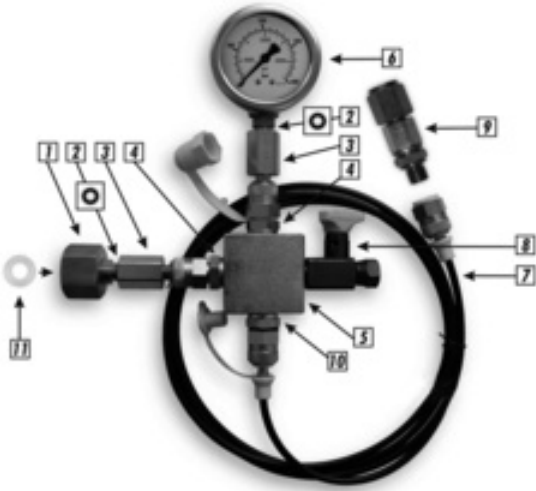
Füllvorrichtung Typ HPCK passend für MINIMESS 1620 Verschraubung mit M16 x 2-Gewinde.
